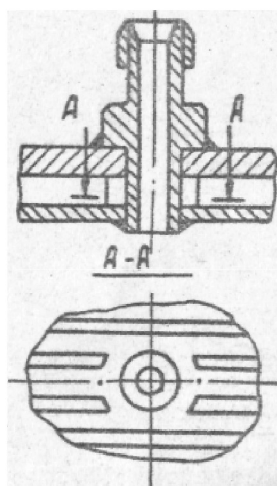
Установка штуцера измерения давления газа в камере сгорания на цилиндрическом участке корпуса
